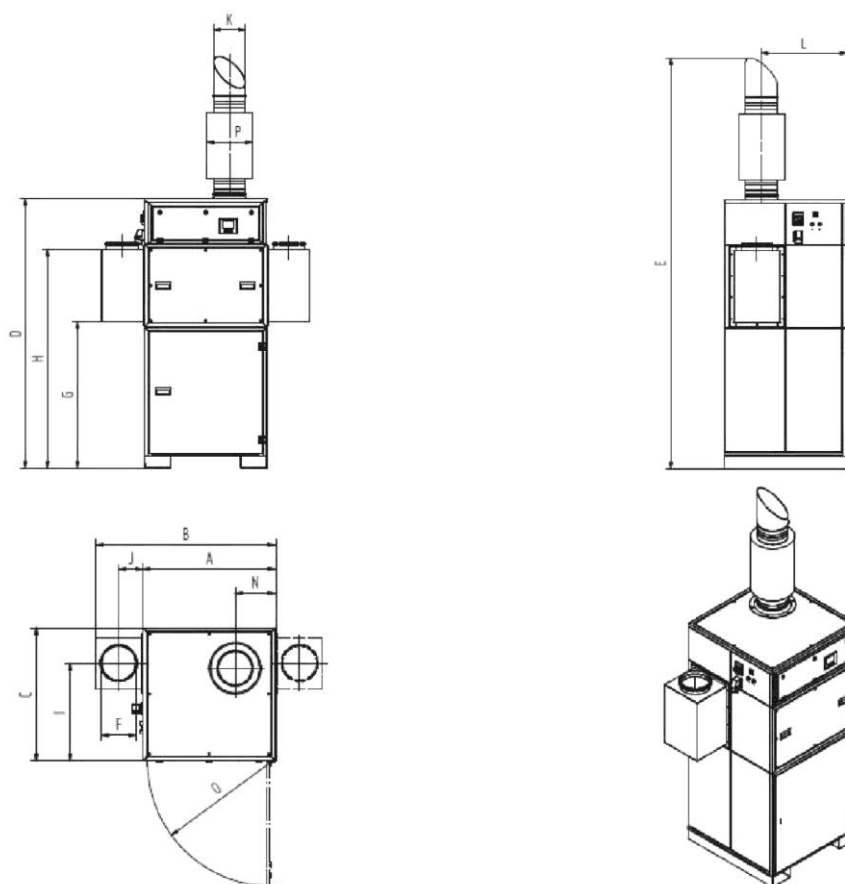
Folha de dimensões 3520, 3710, 3715, 3720, 322014
